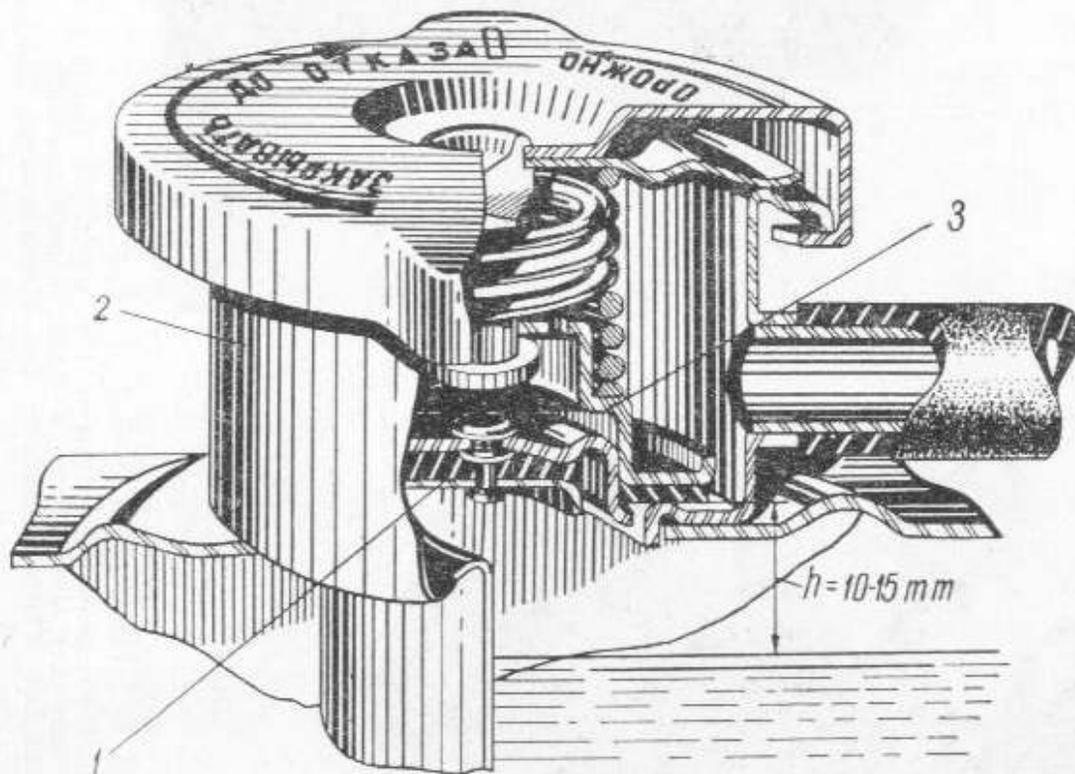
Einfüllstutzen des Kühlers mit Verschraubung:
